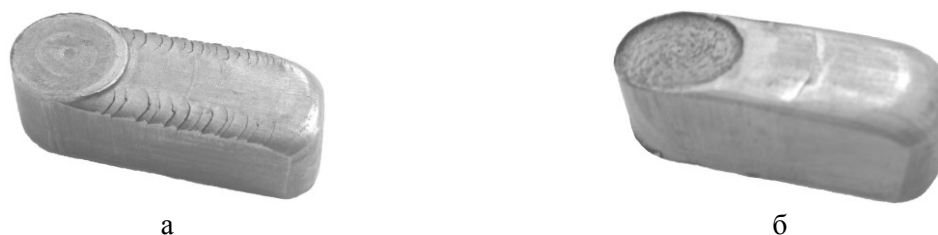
Образцы, полученные по угловому прессованию: а — первый режим; б — второй режим
